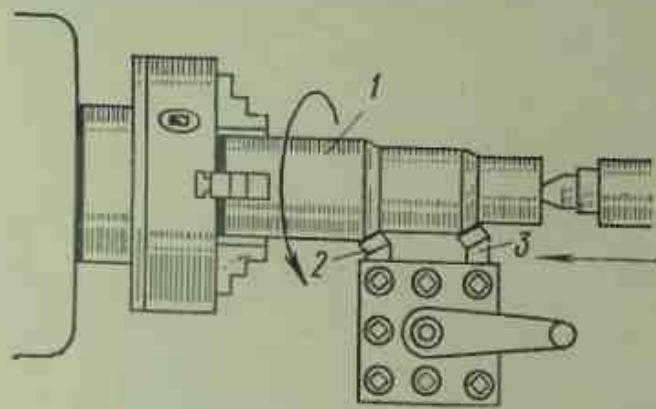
Установка заготовки в патроне с поджимом задним центром:
